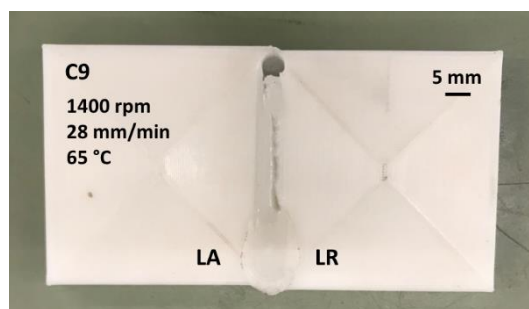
Aspecto visual da superfície das placas soldadas com combinação de parâmetros 9.
